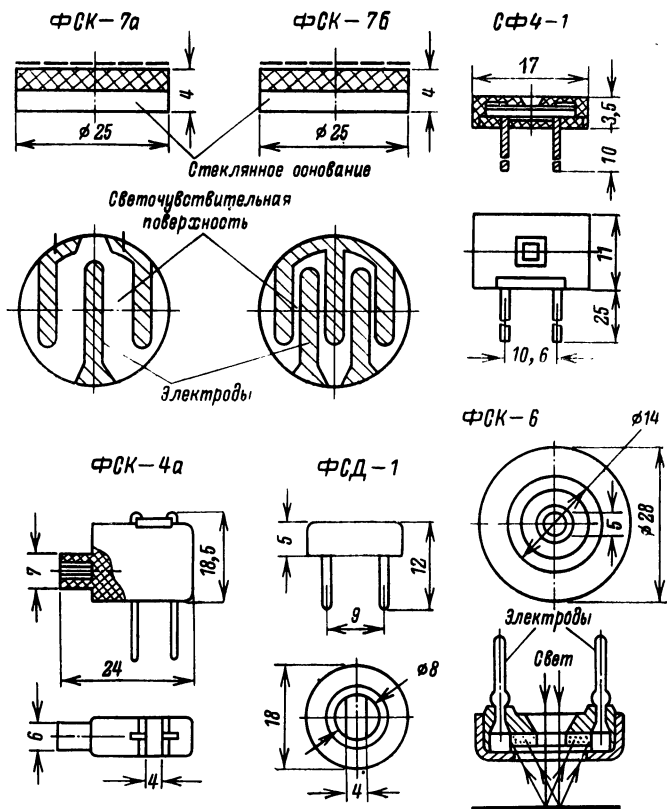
Конструктивное оформление бескорпусных фоторези-
